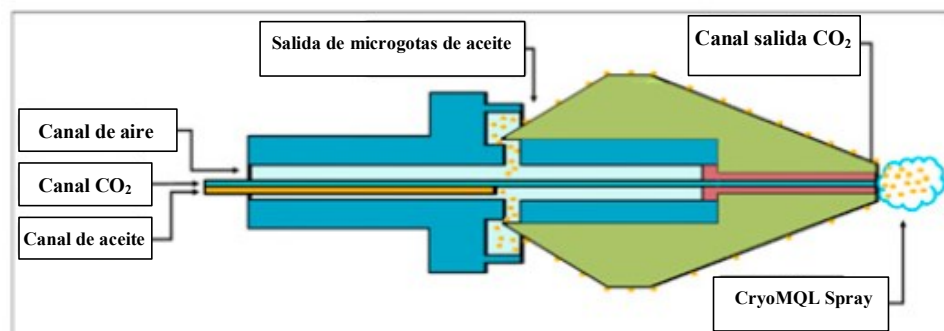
Boquilla de efecto Coanda. Fuente: [4].
